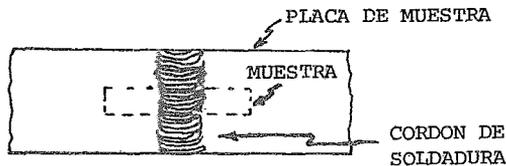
MUESTRA PARA EL ENSAYO DE TENSION.
